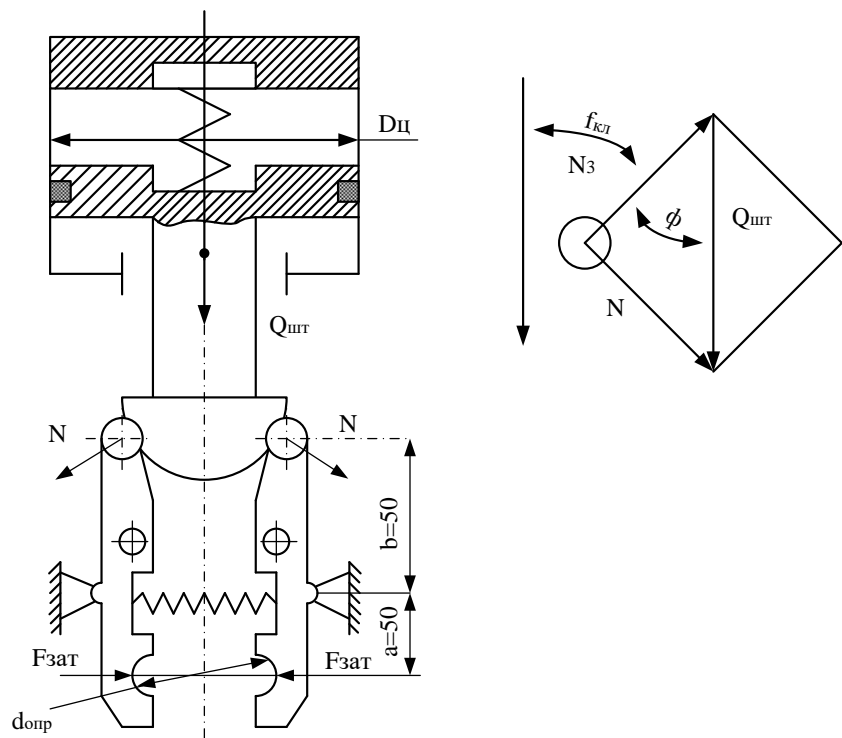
Розрахункова схема приводу затиску інструменту
